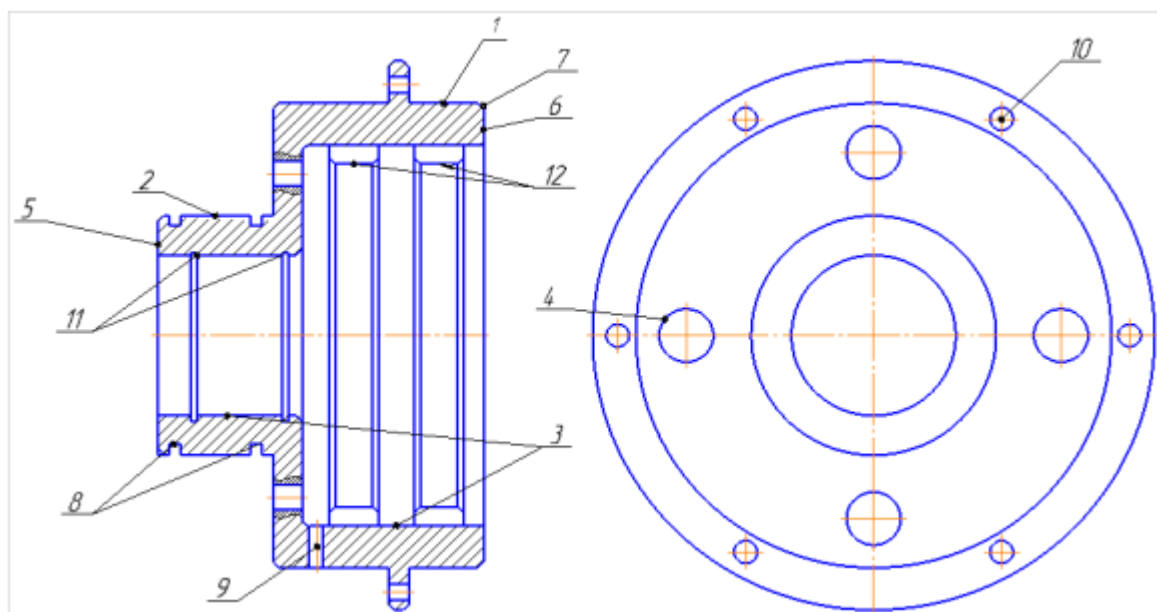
Эскиз детали «Зубчатое колесо»
